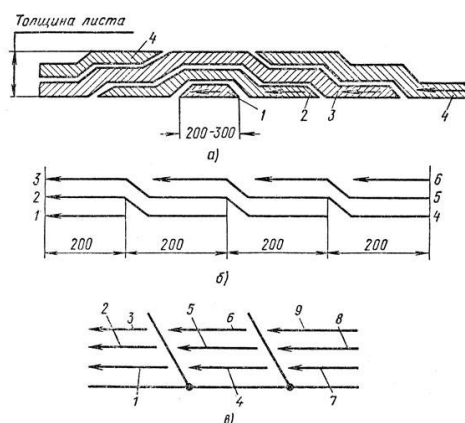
Методы сварки металла большой толщины: а - схема выполнения длинных многослойных швов 'горкой' (1-4 - последовательность наложения швов); б - схема сварки каскадом для выполнения длинных многослойных швов каскадом (1-6 - последовательность сварки); в - схема сварки блоками (1 - 9 - последовательность наложения слоев).
